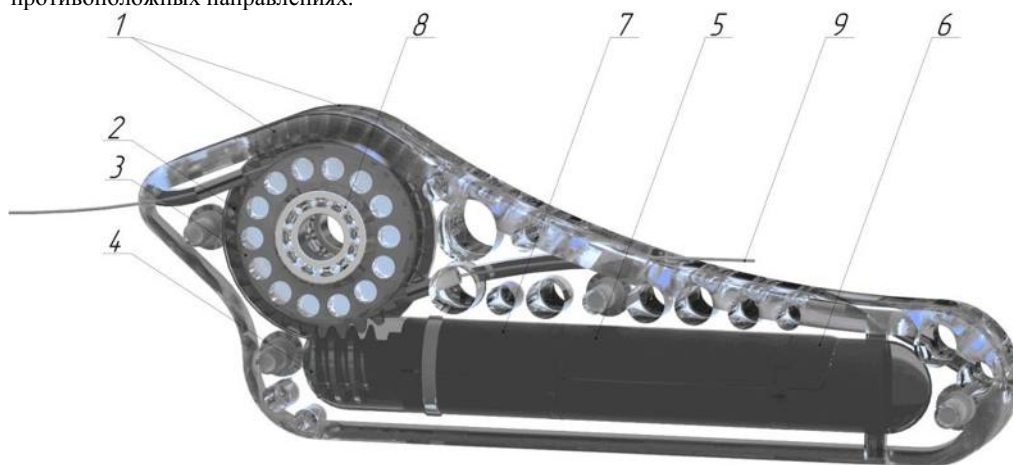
Структурная схема электропривода: 1 – корпусные элементы, 2 - червячное колесо, 3- шкив, 4 - червяк, 5 - электродвигатель, 6 - датчик Холла, 7 - редуктор, 8 - шариковый подшипник, 9 - трос.
